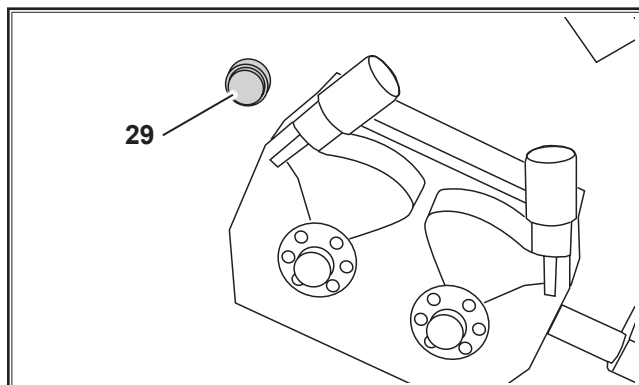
Tlačítko pro zavádění drátu u provedení Basic
